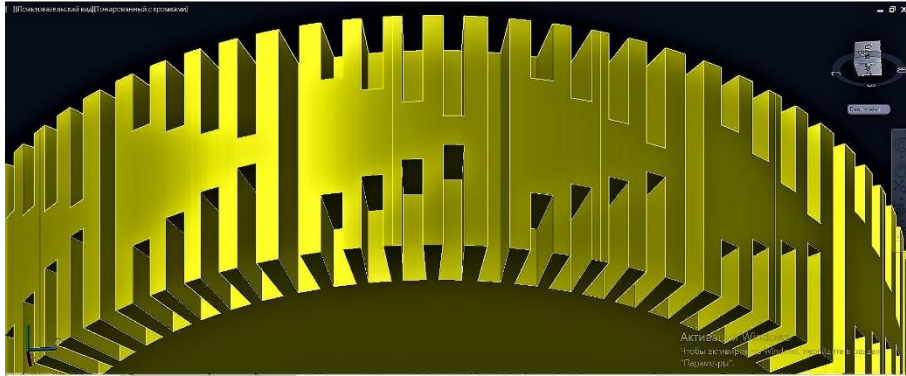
Робоча поверхня круга із наскрізними щілинами та лунками різної довжини, паралельними осі обертання абразивного інструменту
